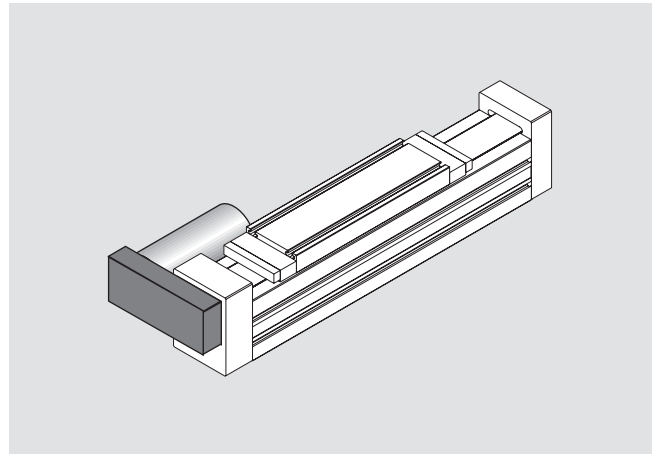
Spindeltrieb mit seitlichem Motoranbau rechts (Montagezustand 04)
